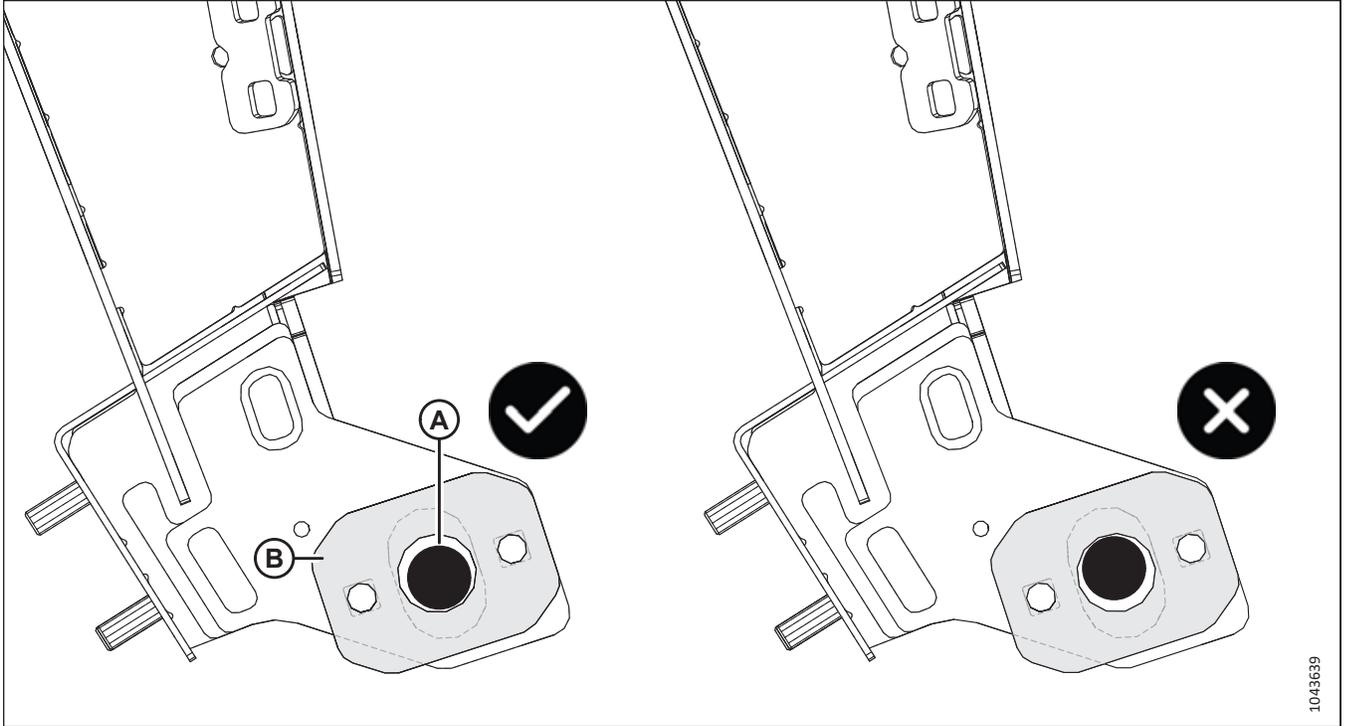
Alignement de la goupille de verrouillage du convoyeur sur une moissonneuse-batteuse John Deere de série X9 ou S7 – Plaque de réglage à position unique
